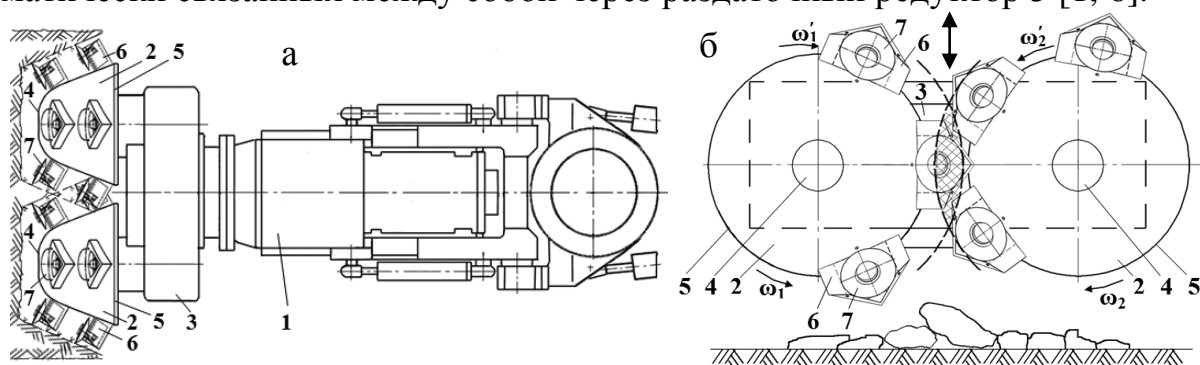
Исполнительный орган с двумя радиальными реверсивными коронками: а – конструктивная схема; б – схема дробления негабаритов
